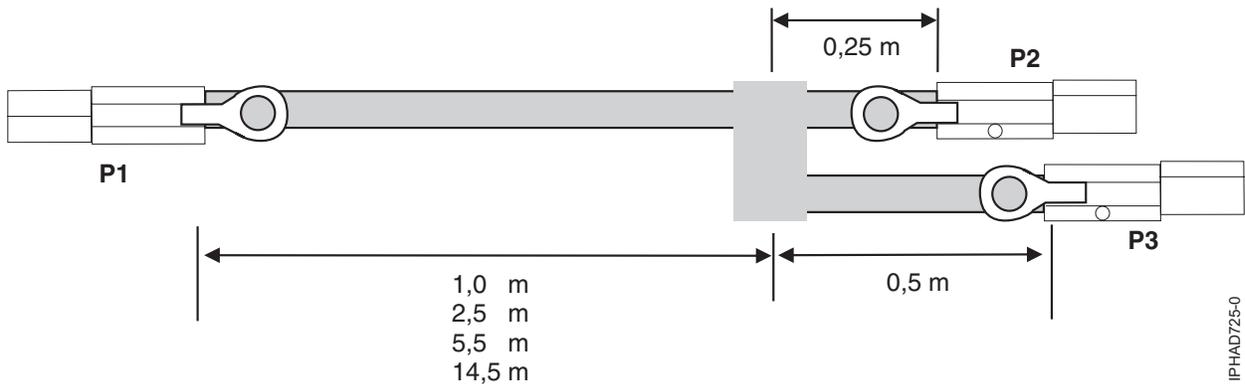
Longitudes de cable de conjunto de cables YO SAS externos
